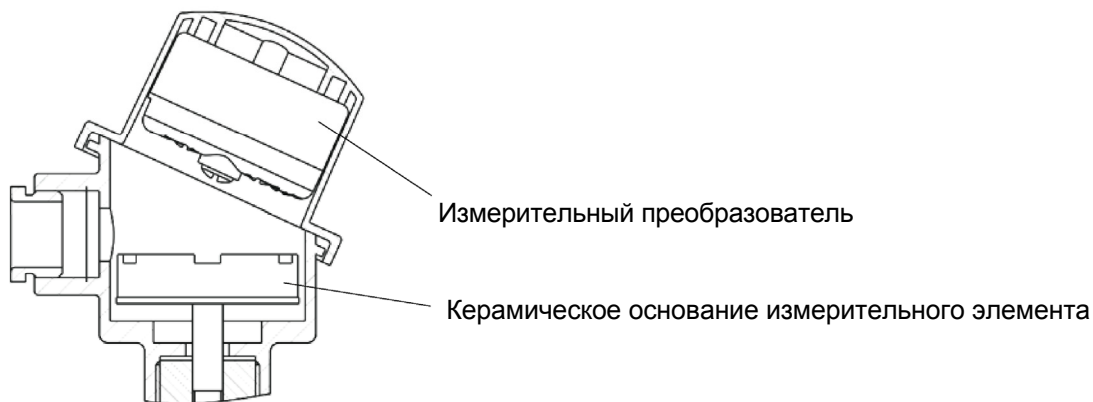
Крепление измерительного преобразователя в крышке соединительной головки
